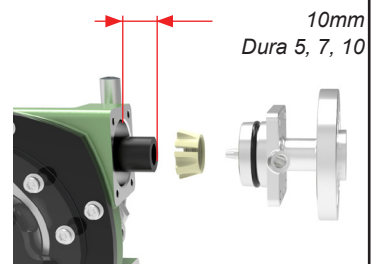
10mm Überstand (geteilter Flansch)
